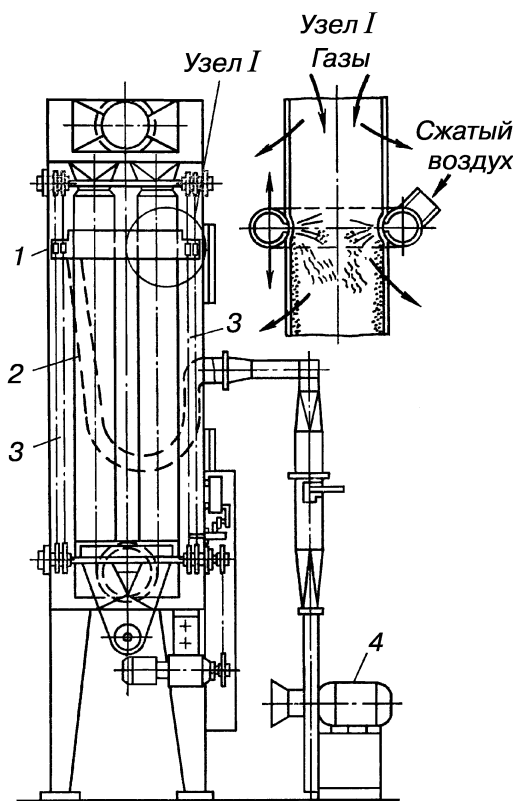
Рукавный фильтр с обратной струйной продувкой: 1 – рама с продувочными кольцами; 2 – гибкий шланг для подвода продувочного воздуха; 3 – цепи для перемещения рамы; 4 – двигатель с высоконапорным вентилятором
